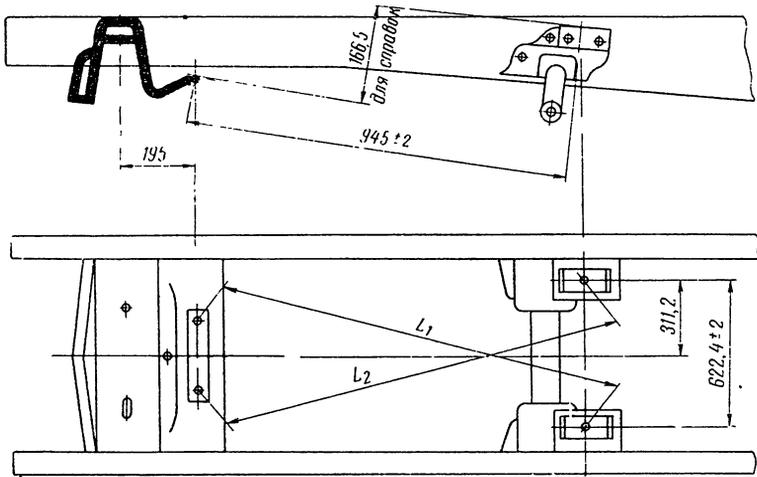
Расположение отверстий для крепления двигателя и радиатора на раме
